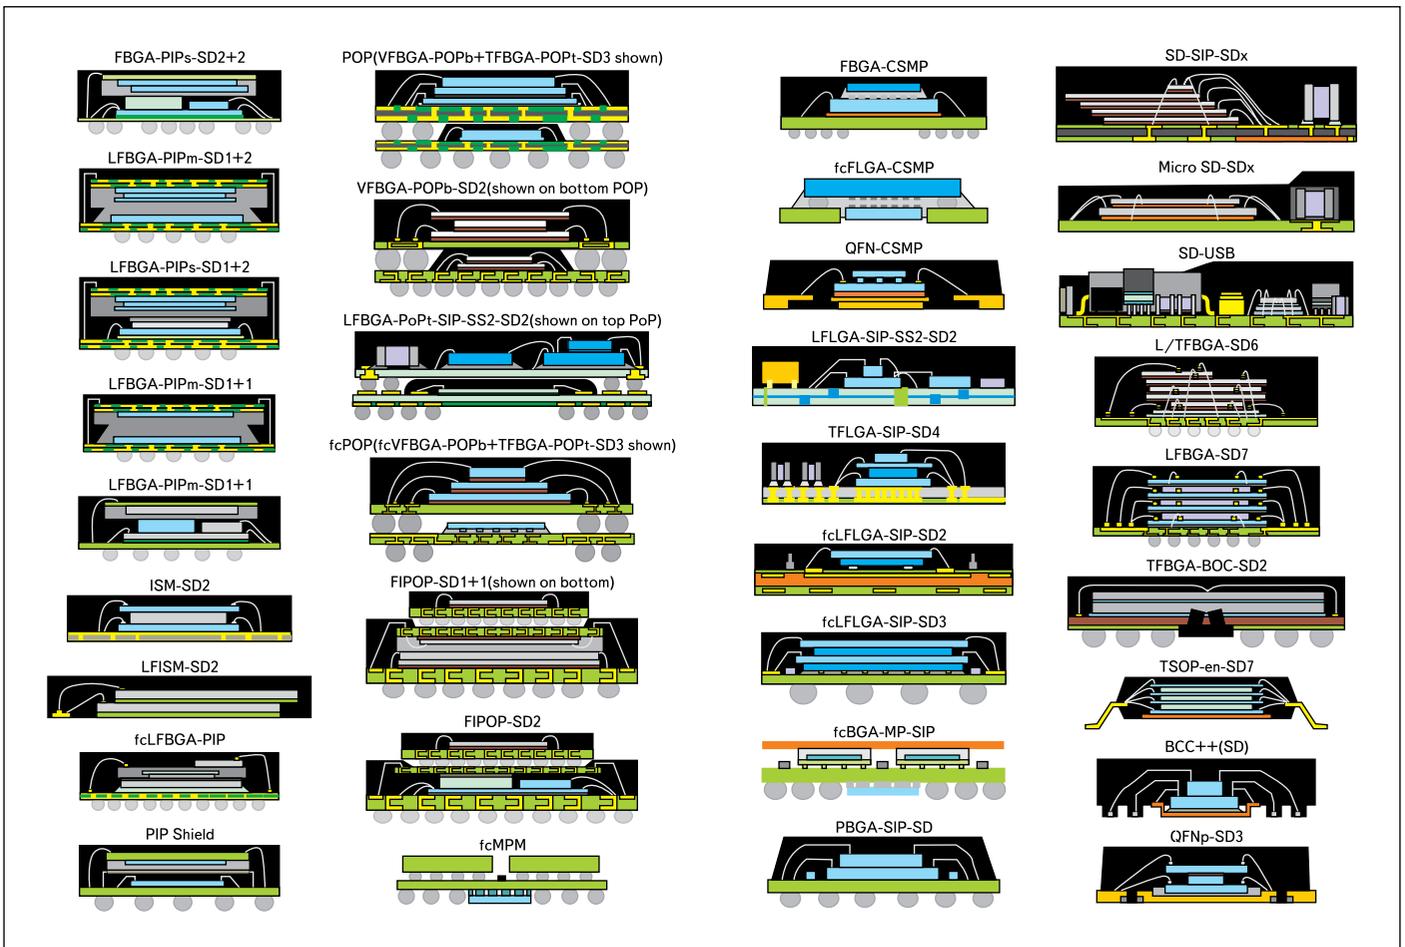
Разновидности корпусов Stack Die с шариковыми выводами, «корпус в корпусе», «корпус на корпусе»
